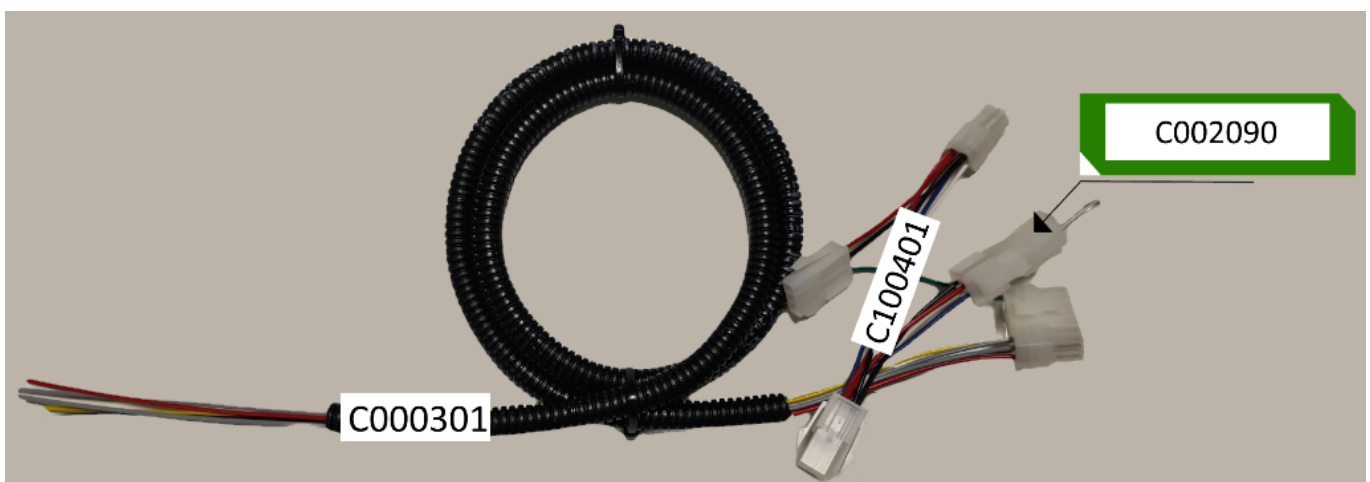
KeyDN-Kabel - Fahrzeug C000301 + C100401 + C002090
